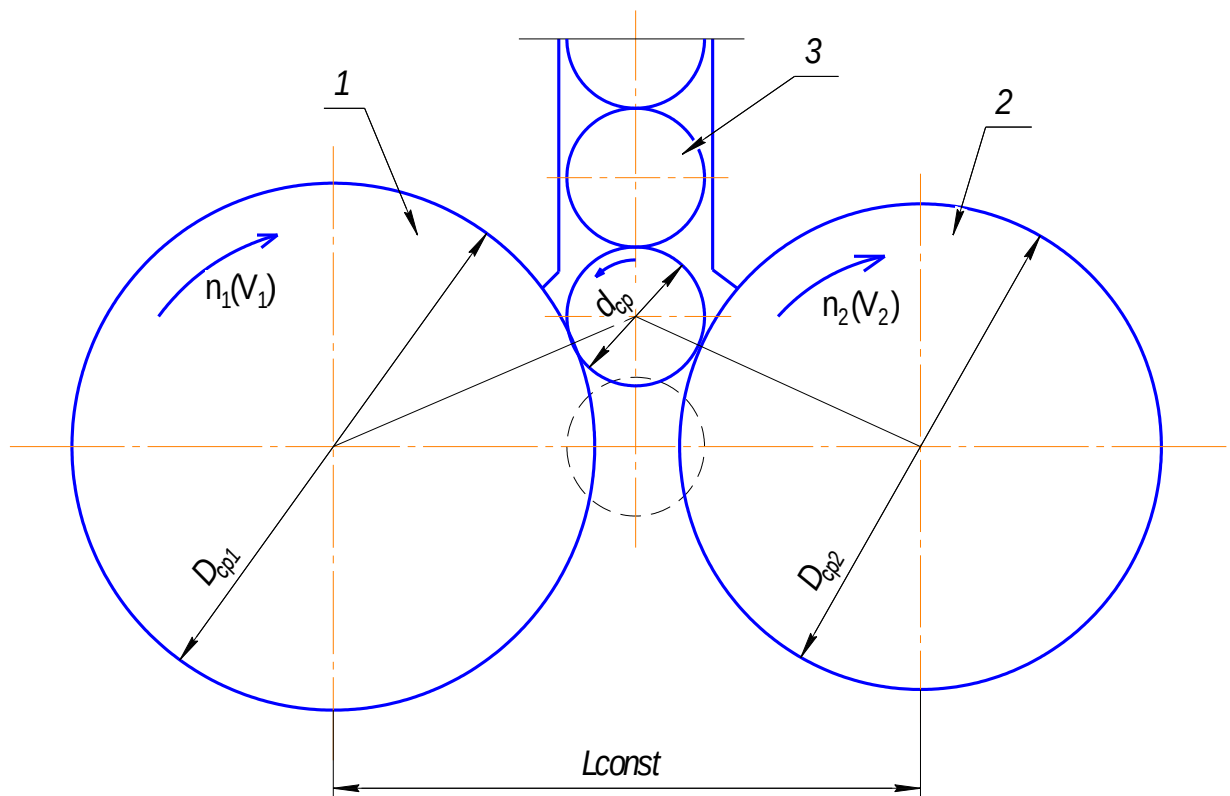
Процесс накатывания резьбы роликами с различными диаметрами
